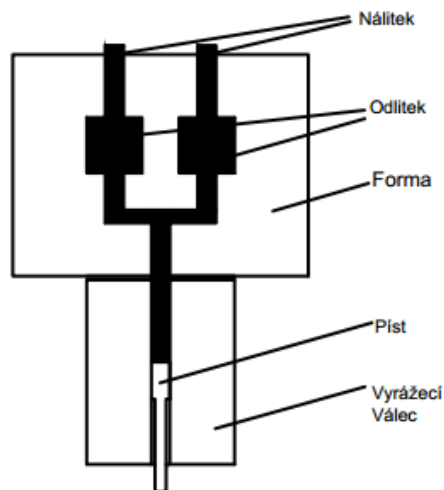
Schéma metody Squeeze casting (odlévání s krystalizací pod tlakem, přímá metoda) [1]
